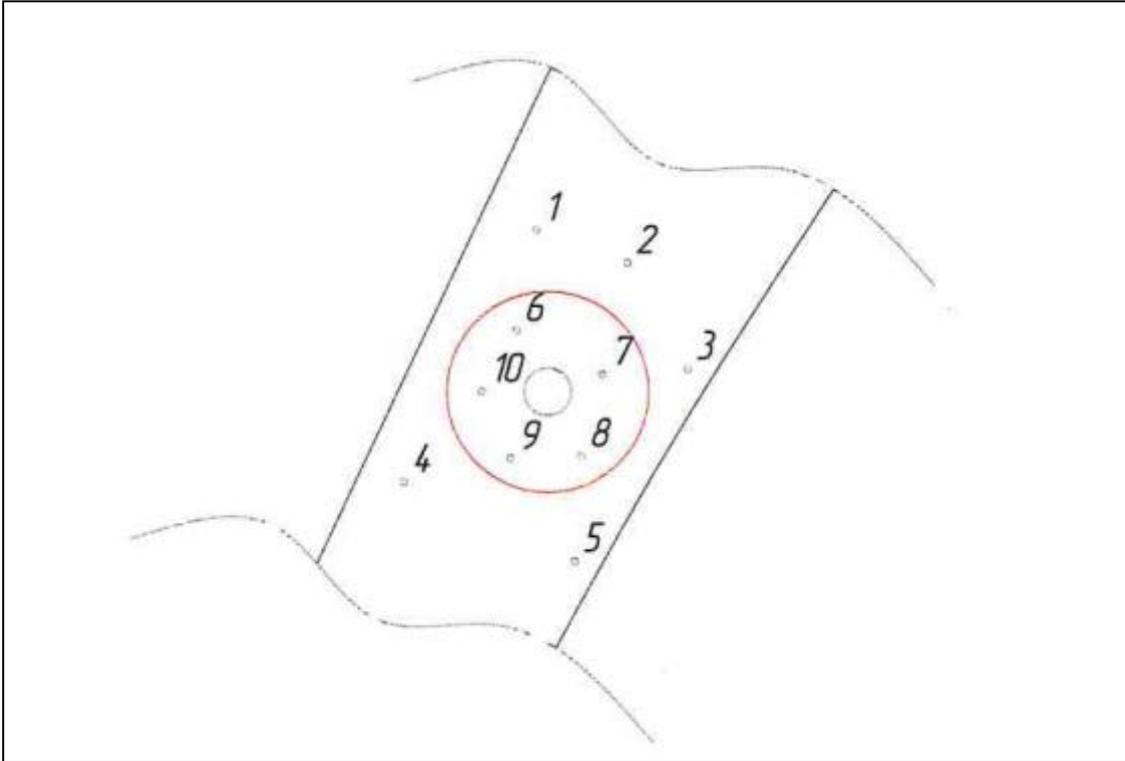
Схема места замера толщины металла корпуса козырькового фальшборта
